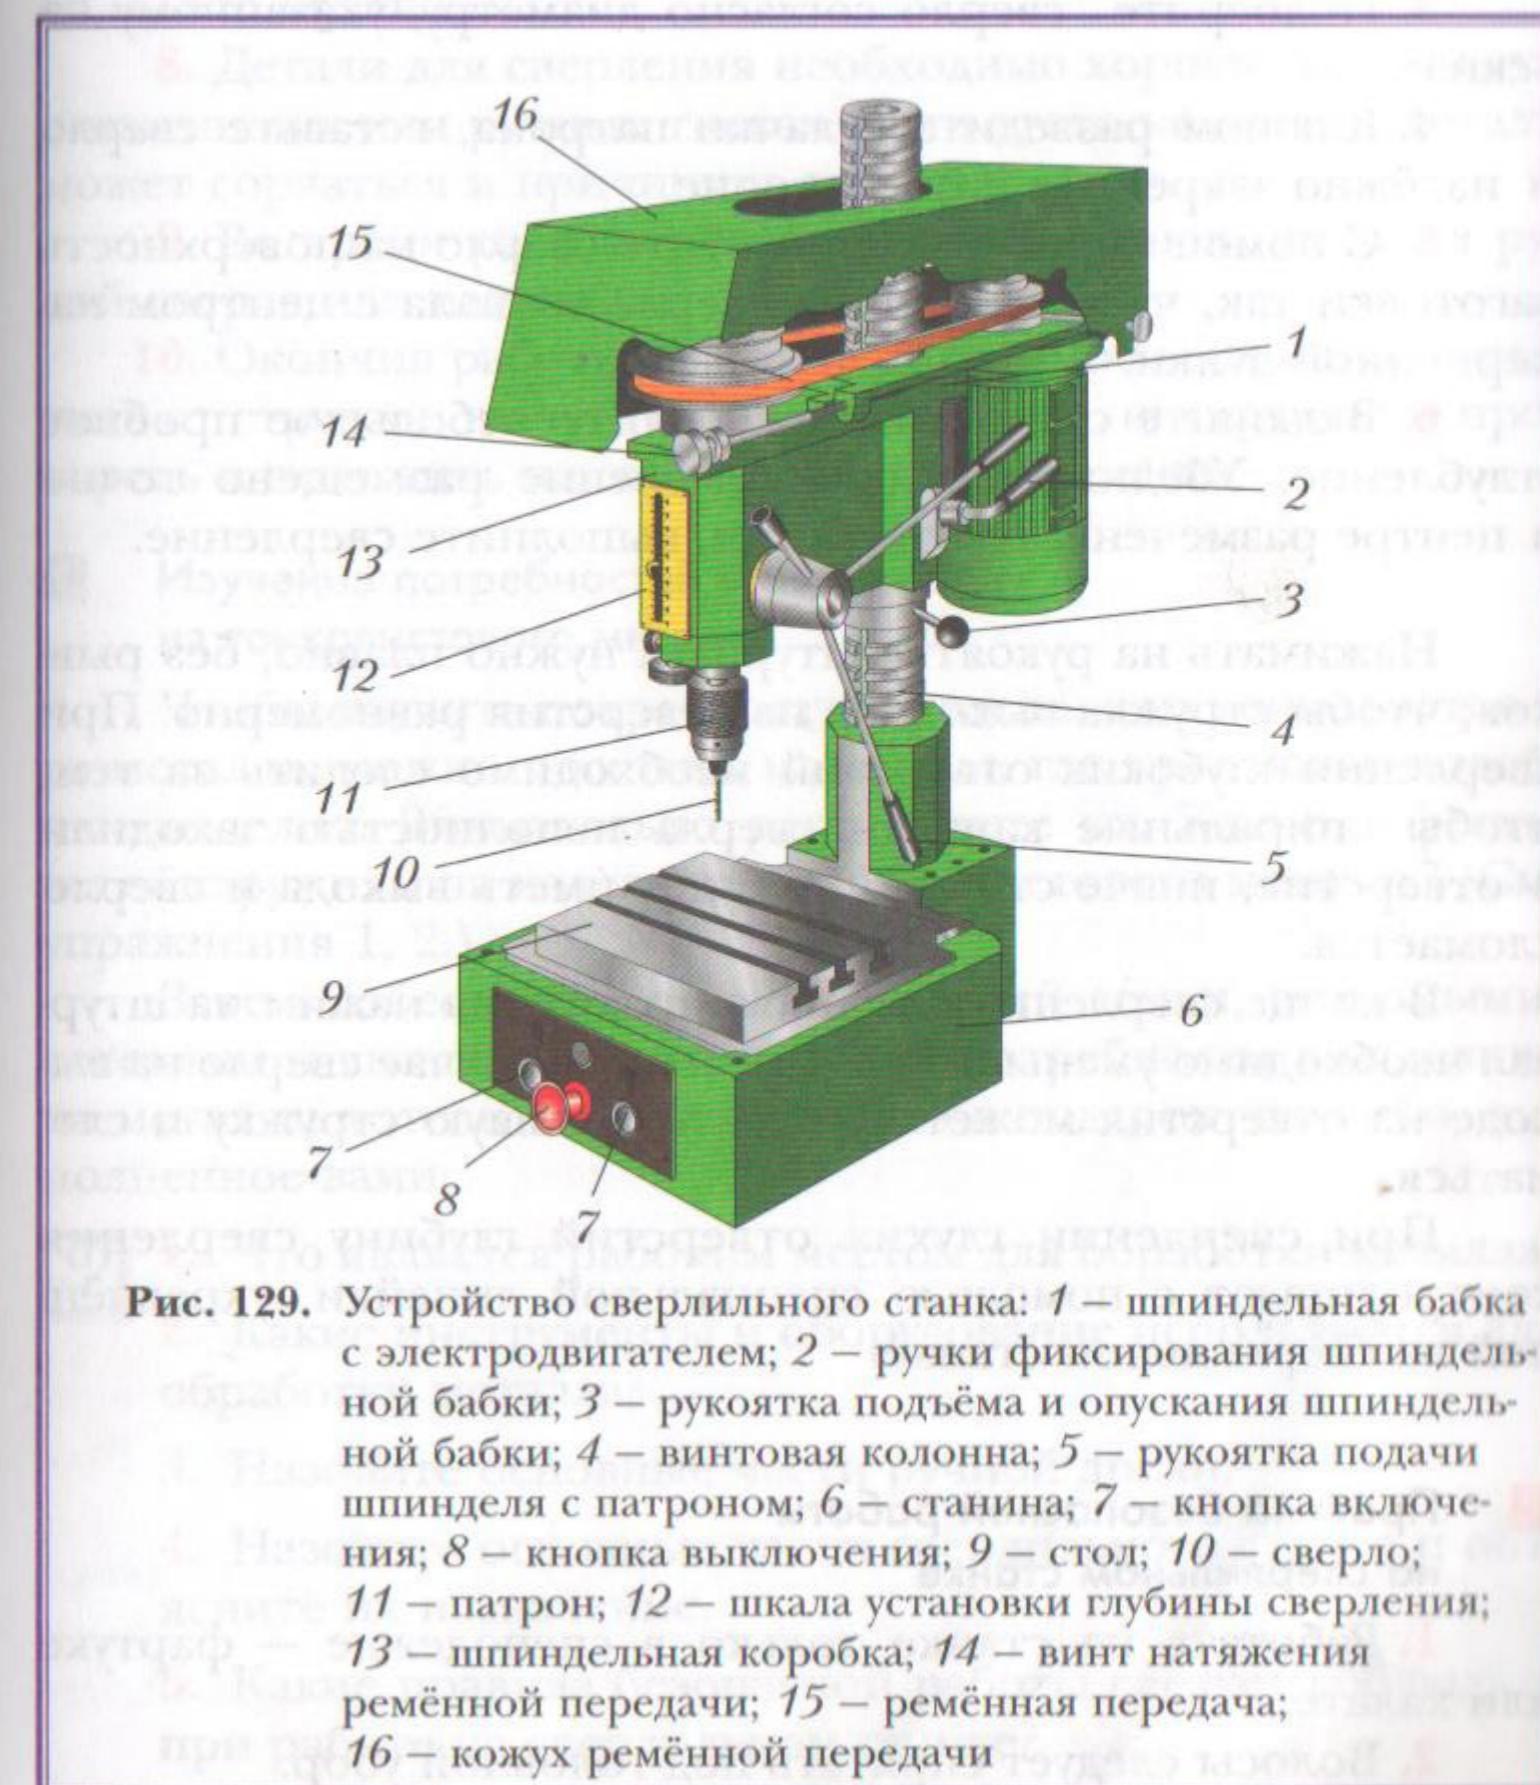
Устройство сверлильного станка: 1 – шпиндельная бабка с электродвигателем; 2 – ручки фиксирования шпиндельной бабки; 3 – рукоятка подъёма и опускания шпиндельной бабки; 4 – винтовая колонна; 5 – рукоятка подачи шпинделля с патроном; 6 – станина; 7 – кнопка включения; 8 – кнопка выключения; 9 – стол; 10 – сверло; 11 – патрон; 12 – шкала установки глубины сверления; 13 – шпиндельная коробка; 14 – винт натяжения ремённой передачи; 15 – ремённая передача; 16 – кожух ремённой передачи
